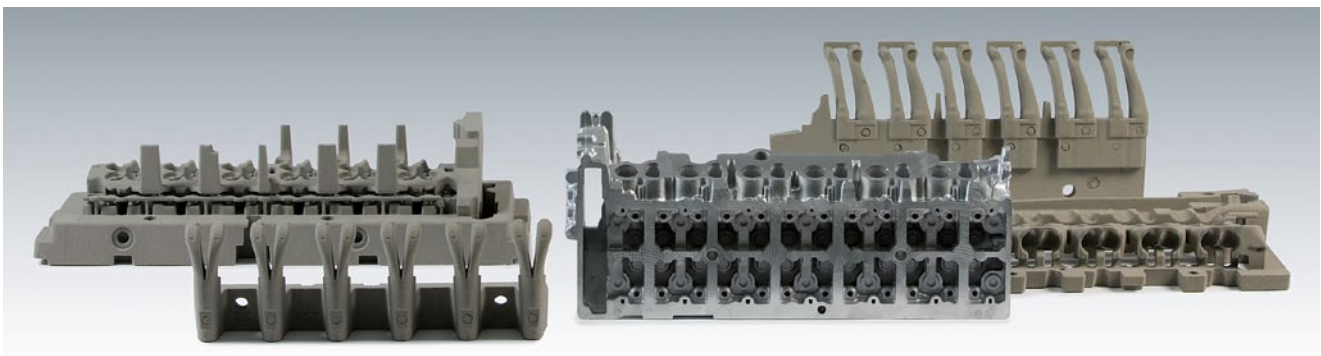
Zylinderkopf für einen 6-Zylinder-Dieselmotor und Sandkerne.
